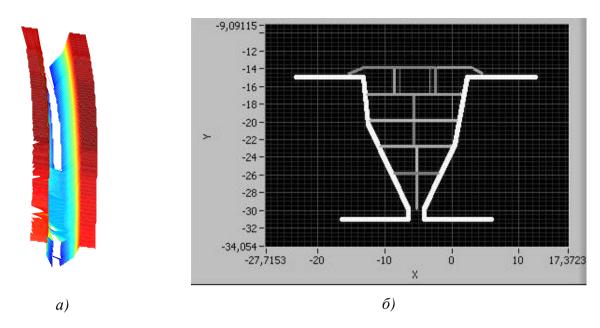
Формирование траектории перемещения сварочной горелки на основе данных лазерной профилометрии. а) — Пространственная модель стыка; б)- раскладка валиков шва при многослойной сварке.
